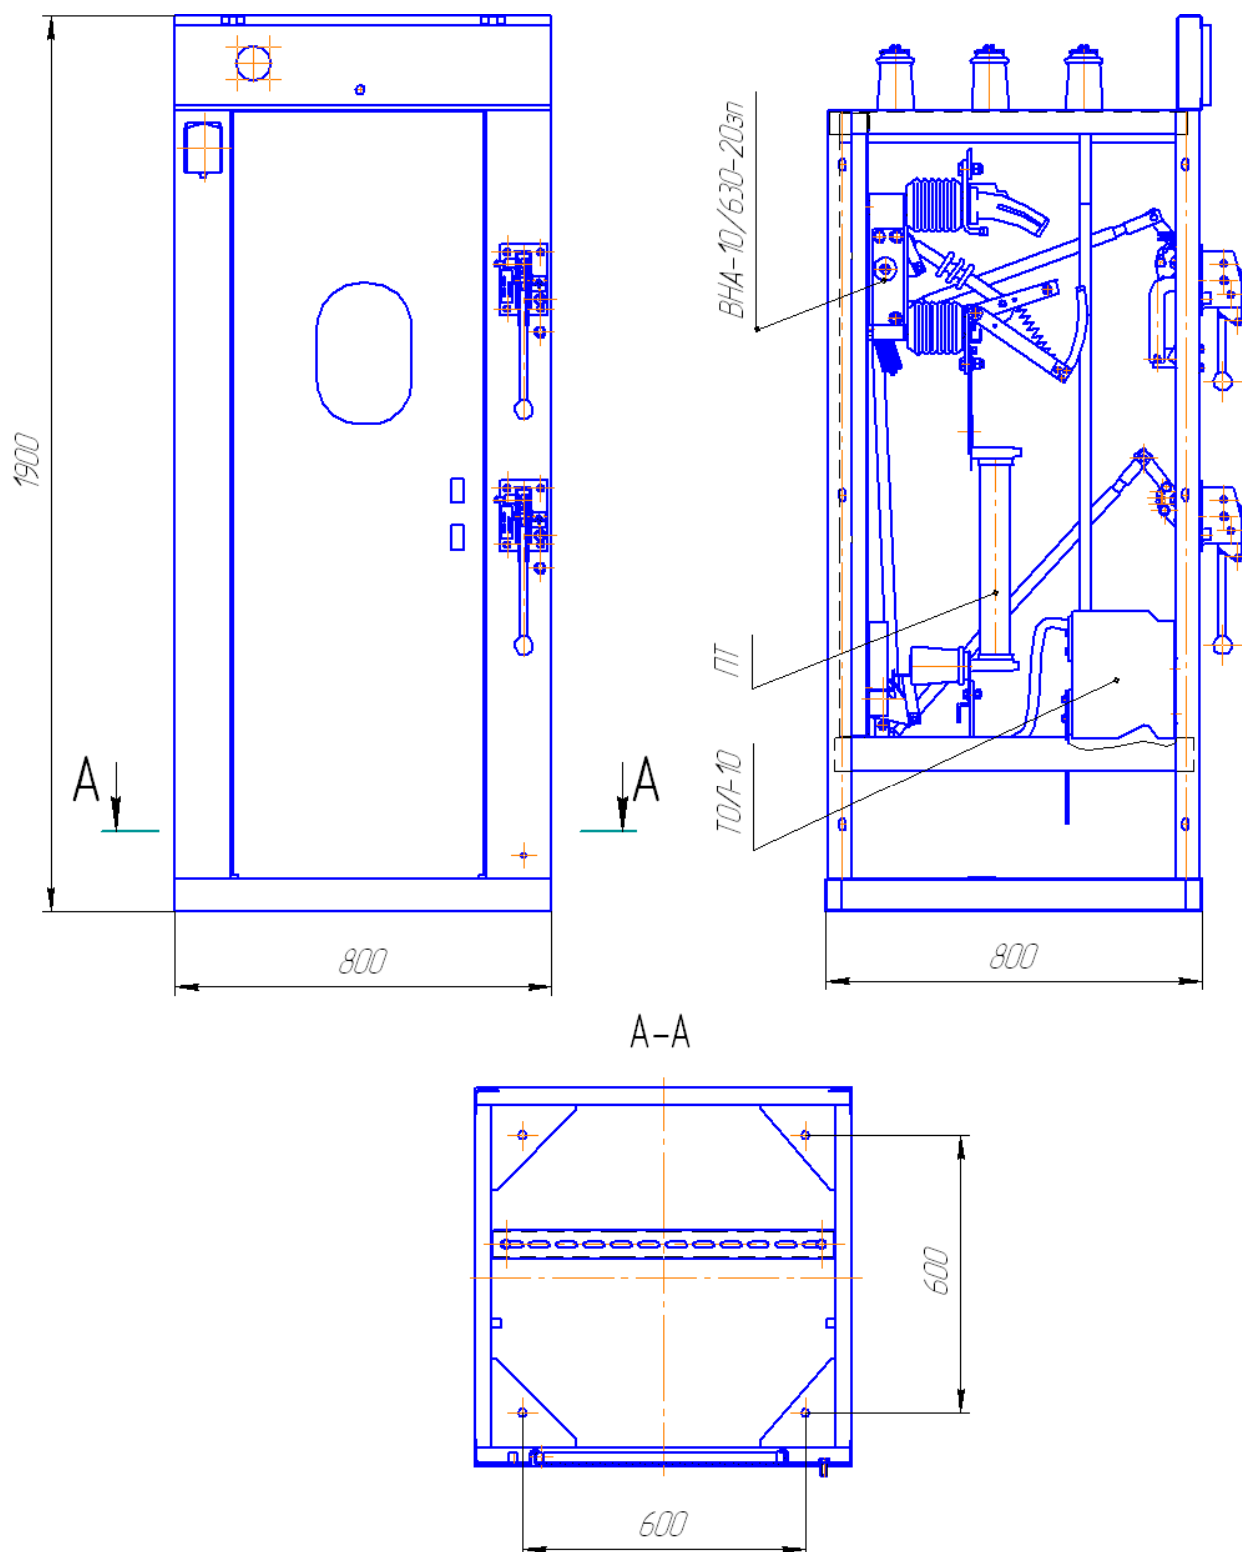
Габаритные и установочные размеры ячейки КСО-393М-05
